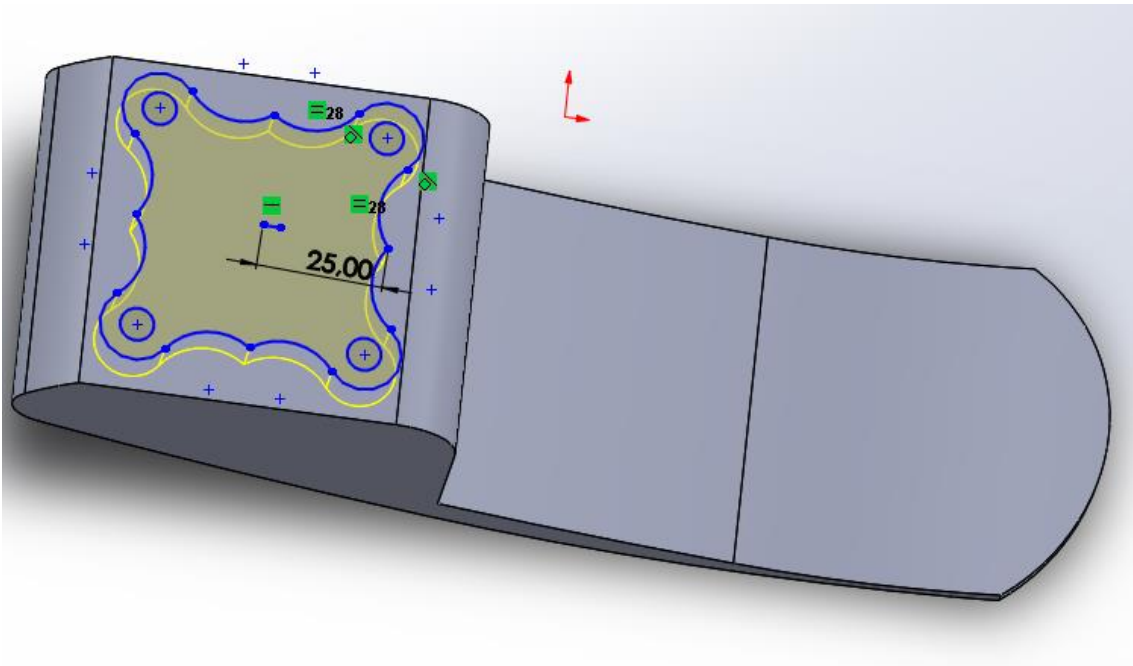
Cut-Extrude do encaixe do dispositivo de fixação.
